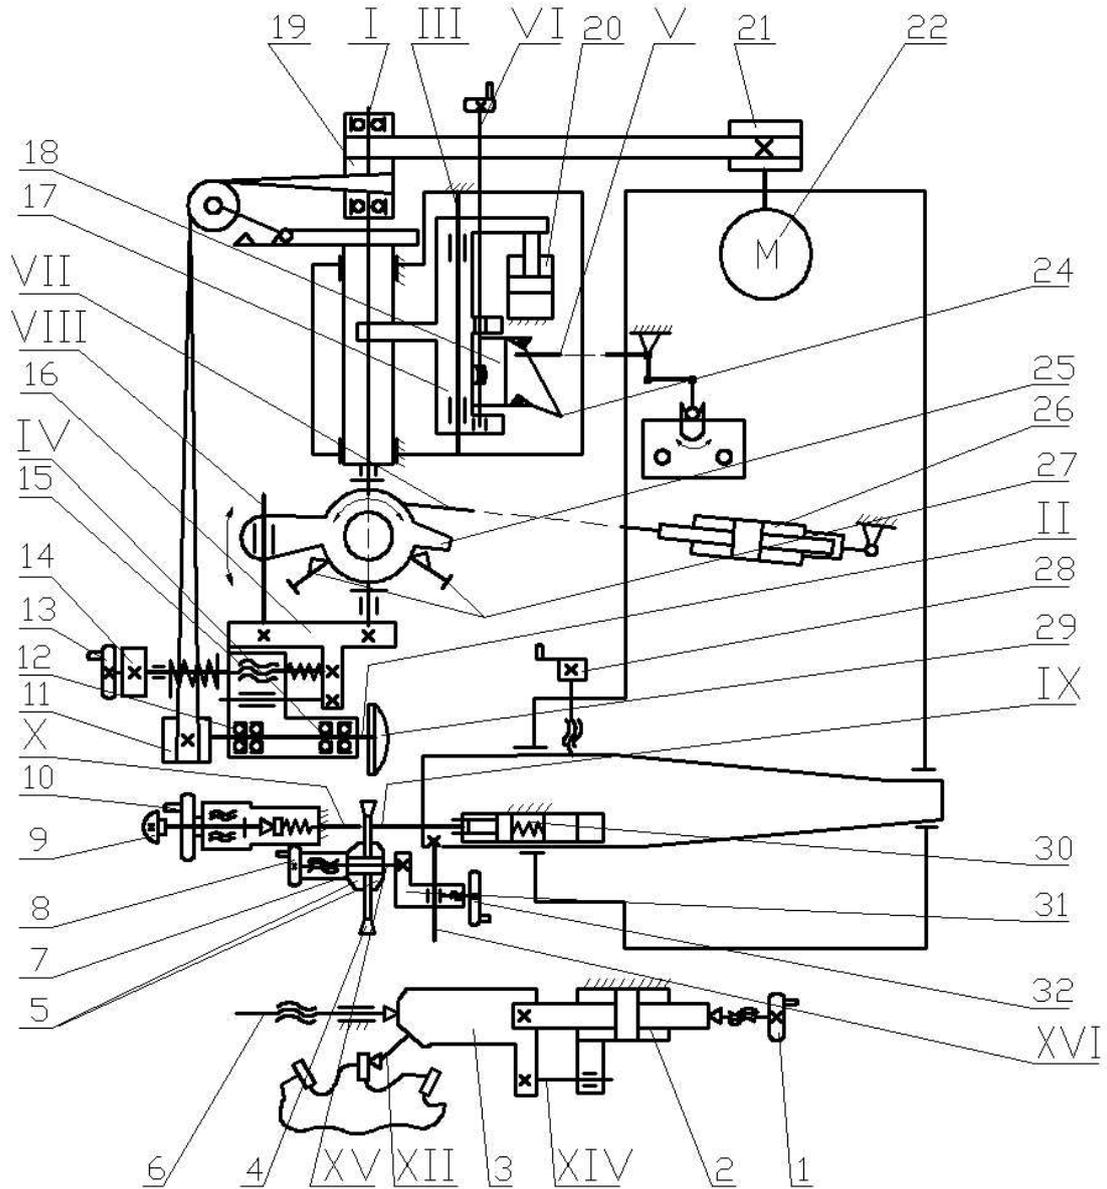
Кинематическая схема станка ТчПТ-4
